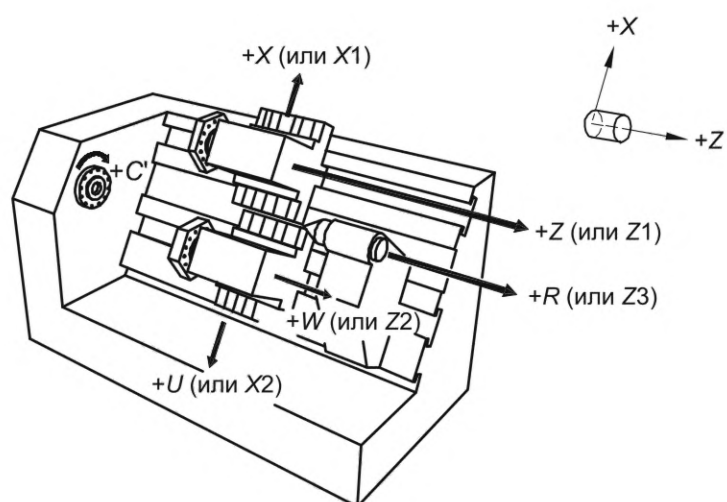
Токарный станок с двумя револьверными головками с программируемой центрирующей бабкой
